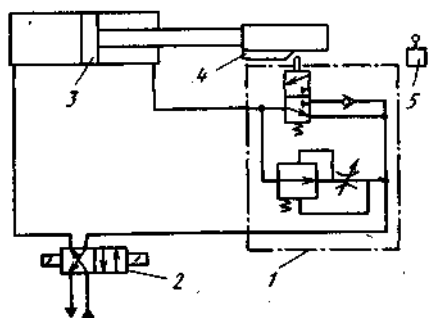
Схема гидропривода с устройством для автоматического управления по циклу: «быстрый подвод — рабочий ход — быстрый отвод — остановка»
